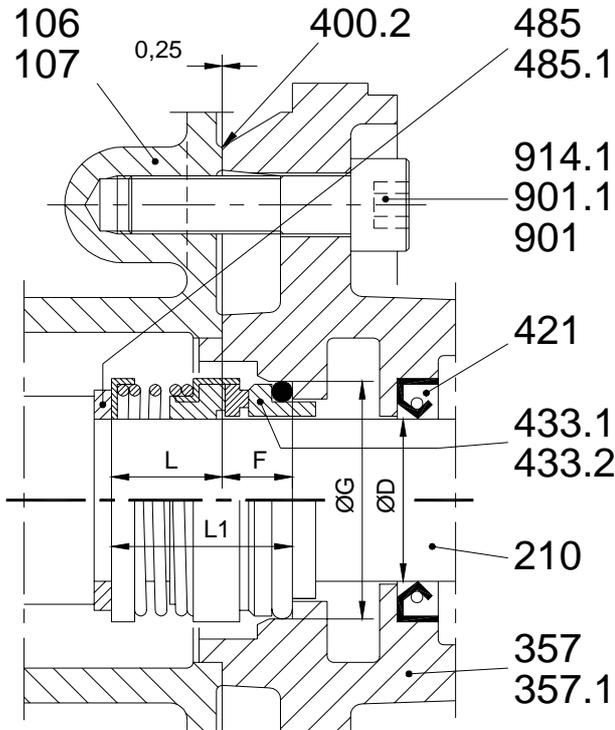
Diseño típico de los cierres mecánicos con dimensiones válidas para ambos lados
